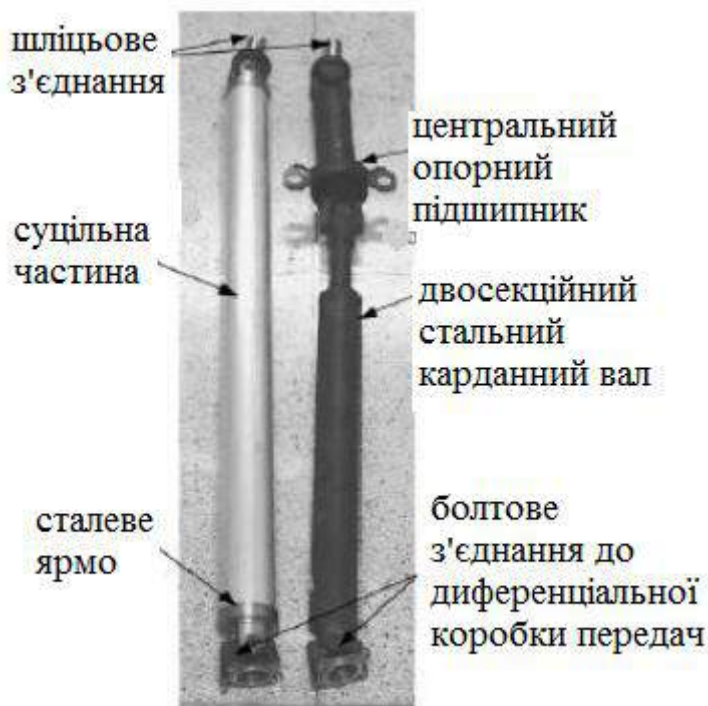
Звичайний карданний вал та композитний карданний вал.
